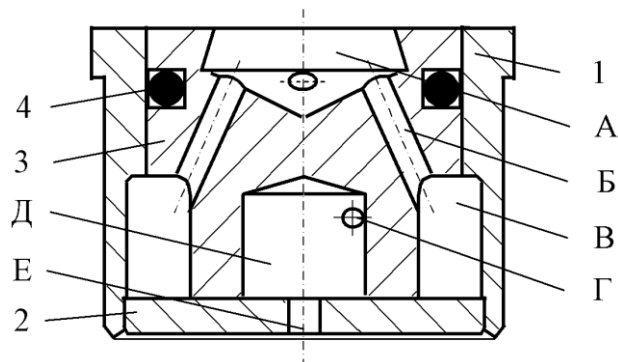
Загальний вигляд і конструктивна схема відцентрового розпилювача: 1- корпус; 2- сопло; 3- завихрювач; 4- гумове кільце.
